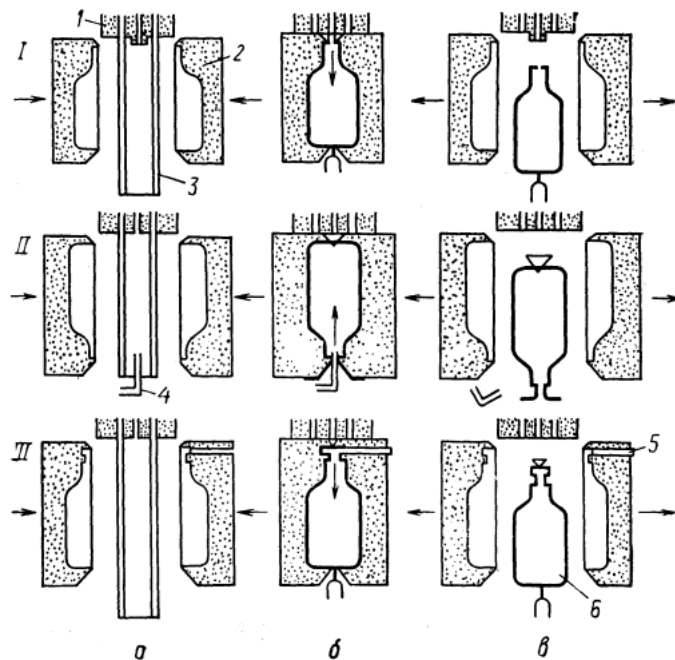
Схеми роздування заготовки стисненим повітрям, що подається зверху (I), знизу (II) або крізь дуттьову голку (III): а – змикання форми; б – роздування заготовки та охолодження виробу; в – розмикання форми й знімання виробу; 1 – екструзійна головка; 2 – півформа; 3 – заготовка; 4 – дуттьовий ніпель; 5 – дуттьова голка; 6 – виріб
